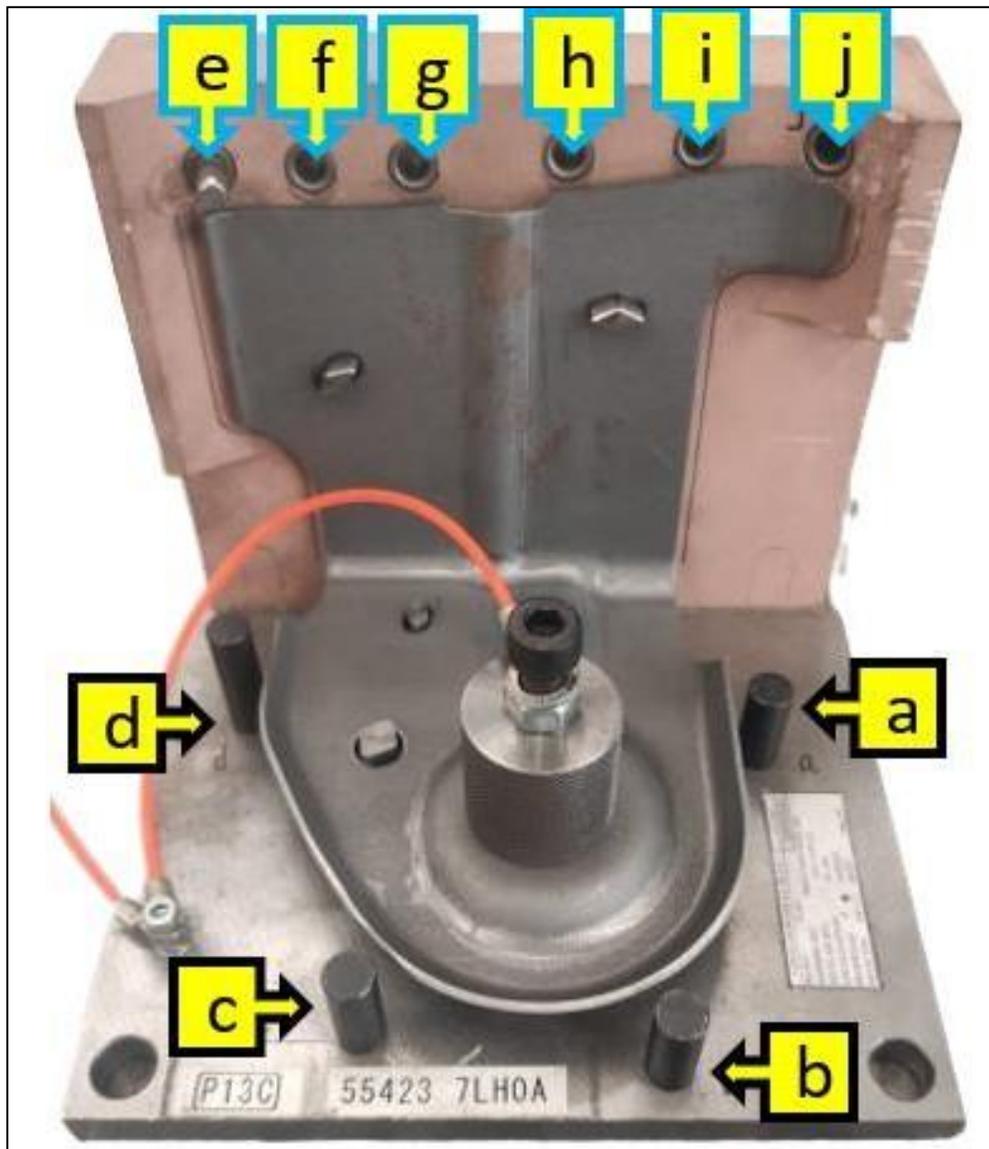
Jig de calidad para parte estampada Fuente YMEX 2024
